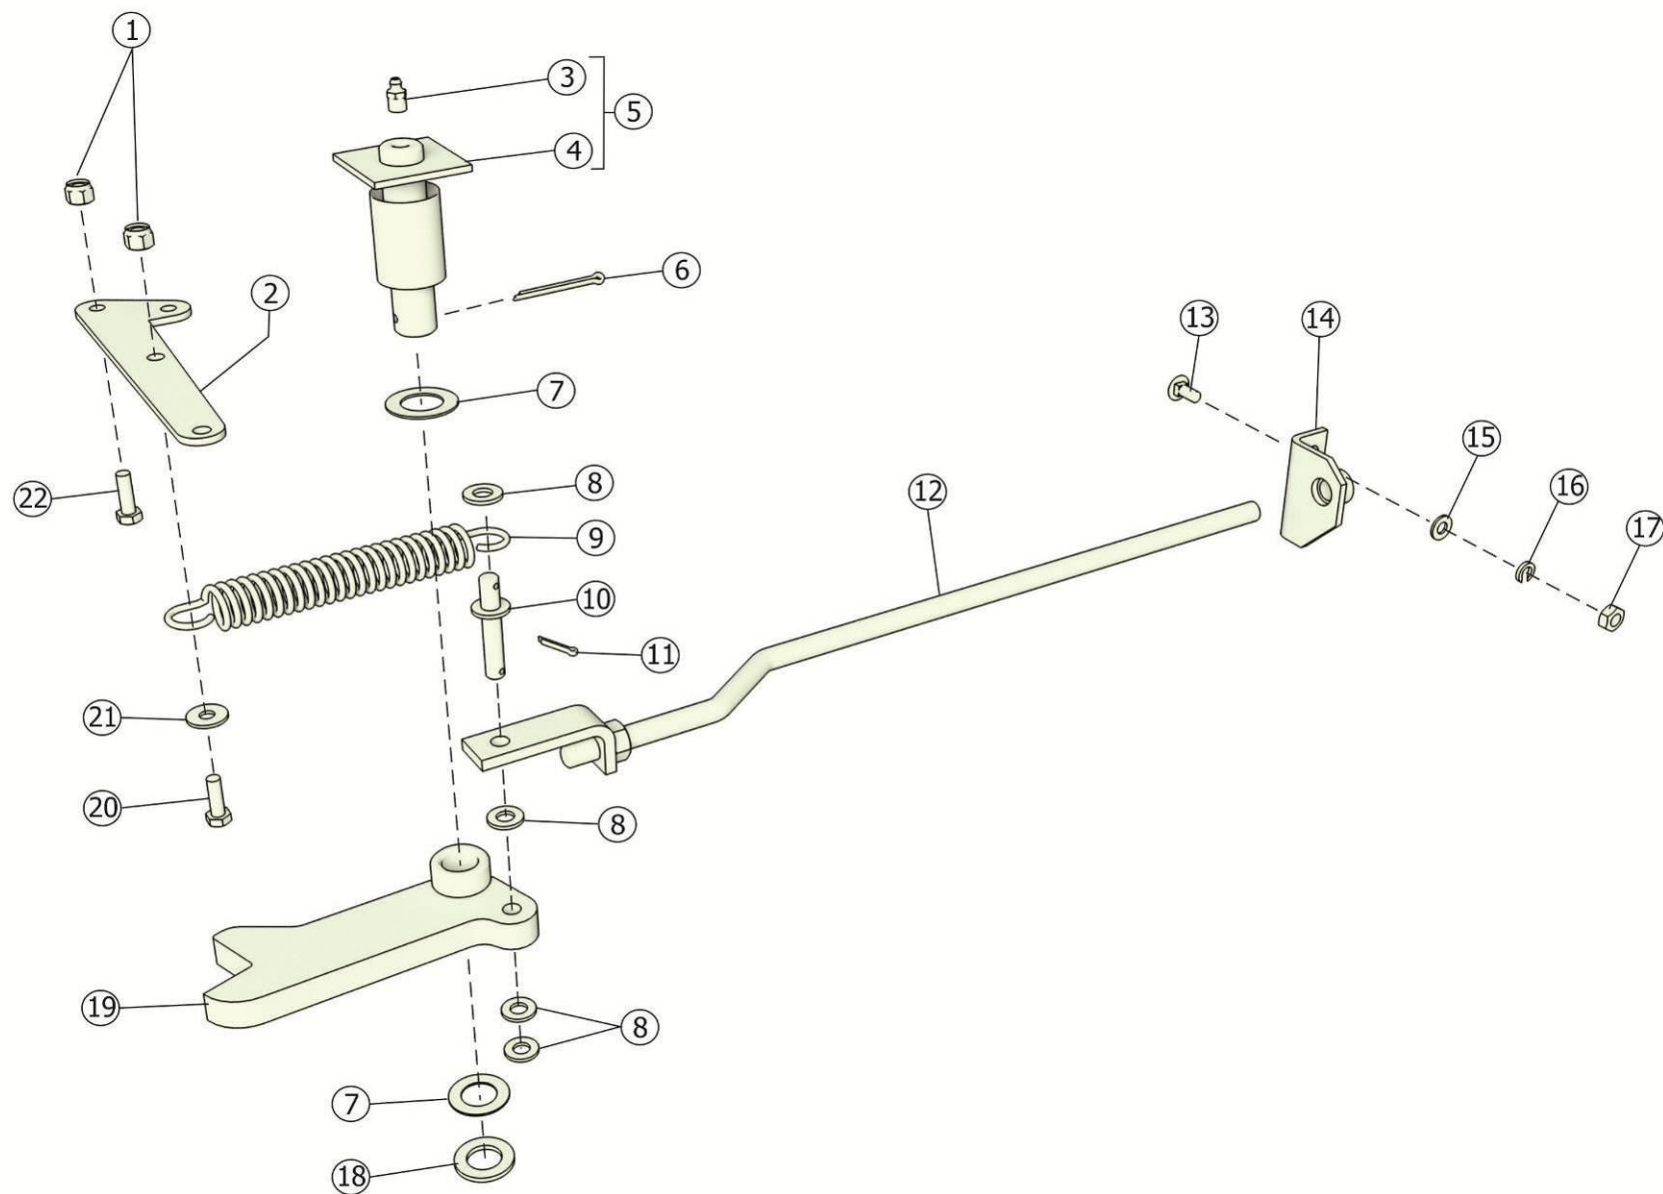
Установка предохранителя ППТ-041.01.300
